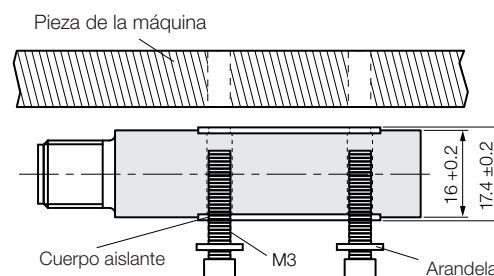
Montaje de la cabeza de sensor con cuerpo aislante
